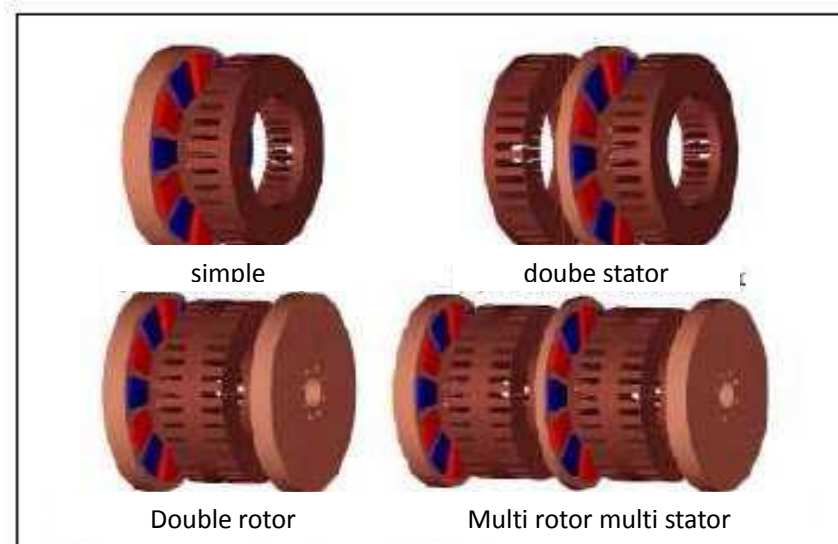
Vue d'une machine à flux axial (différentes configurations)
